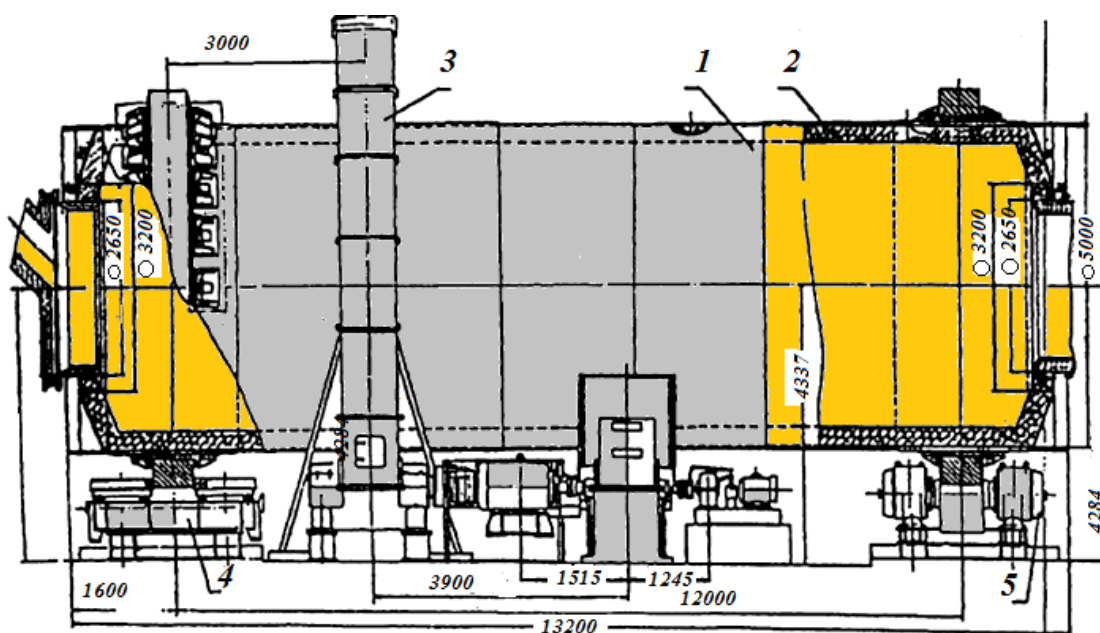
Барабанный реактор: 1- корпус реактора, 2-футеровка (обмуровка),3 привод,4-5 подшипники
